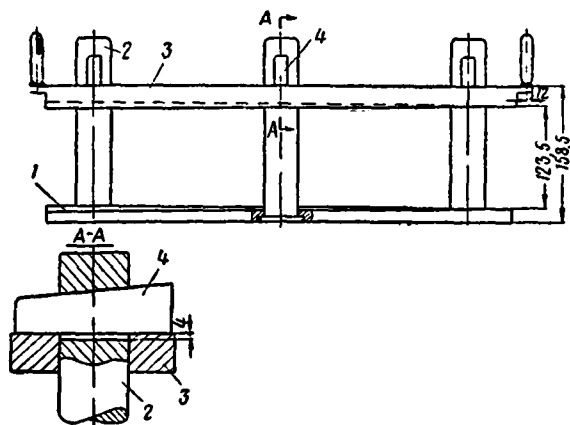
Приспособление для выпечки межвитковой изоляции катушек:
